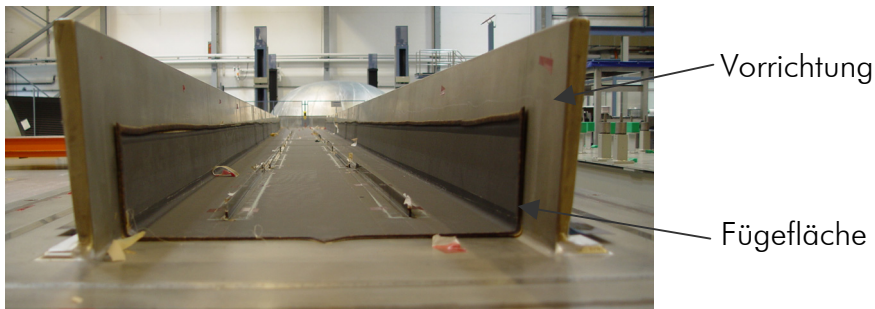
Werkzeugvorrichtung eines A380-Holmes (Quelle: Airbus)
